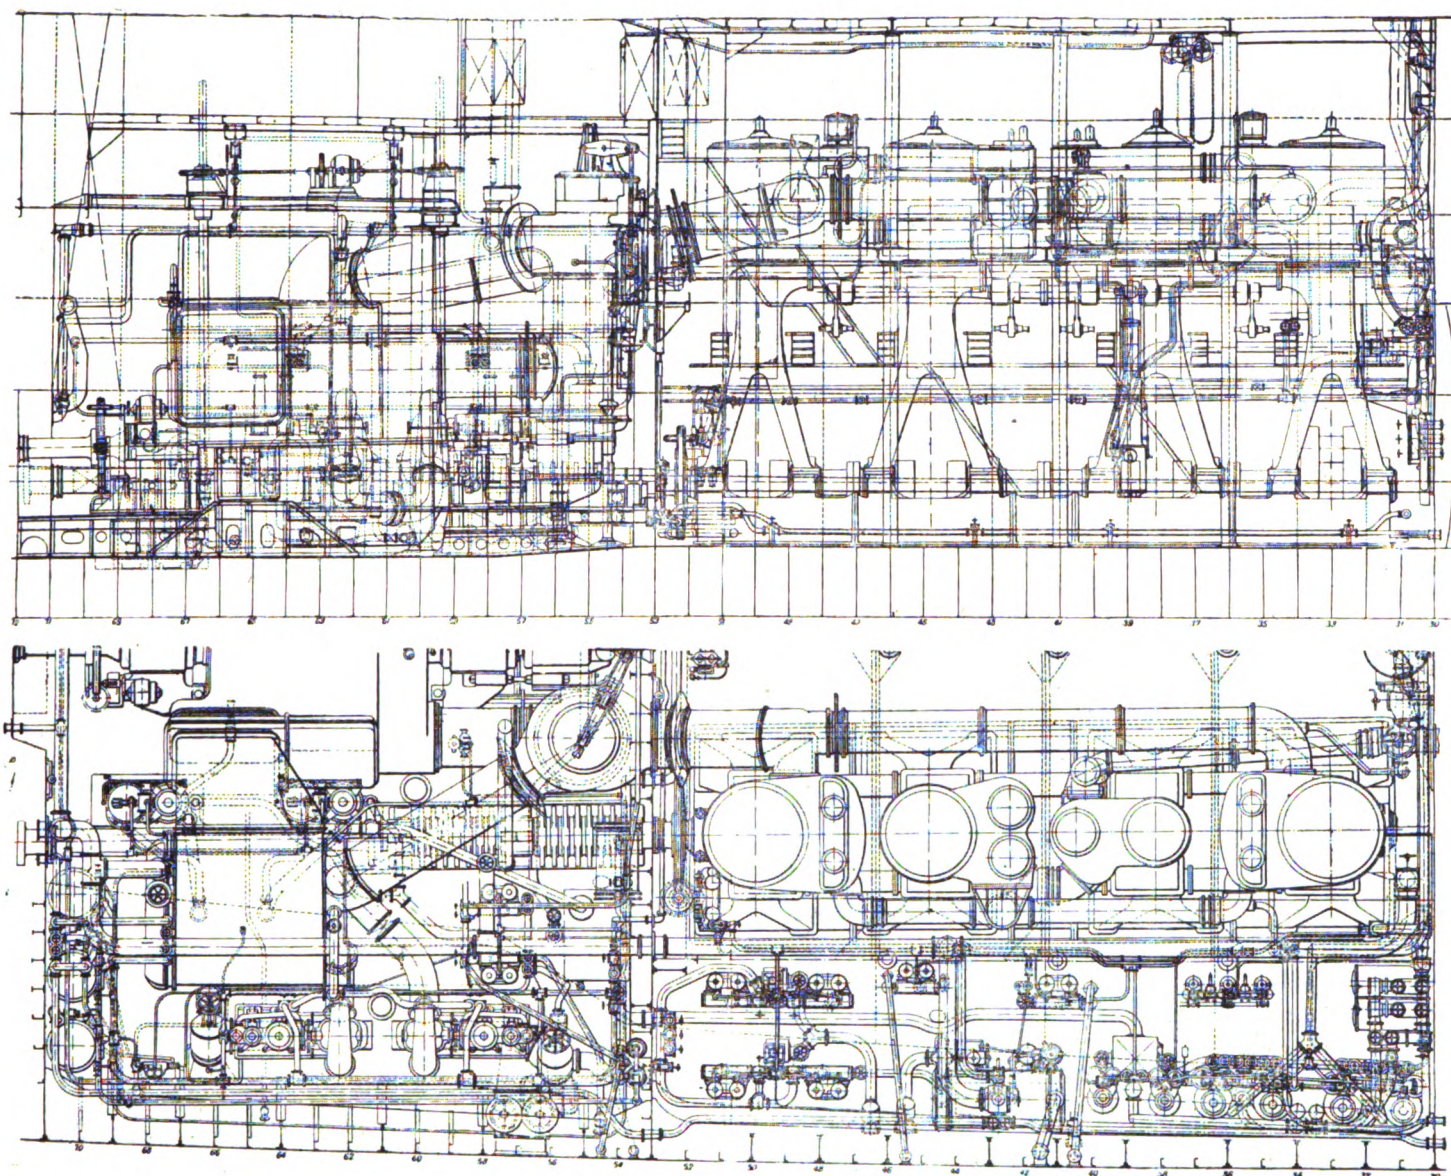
e 2. — Apparato motore - Elevazione e pianta.
